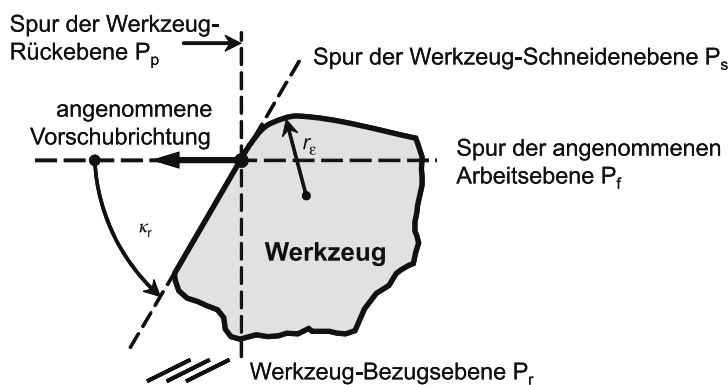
Die Lage des Werkzeug-Einstellwinkels κ_r
